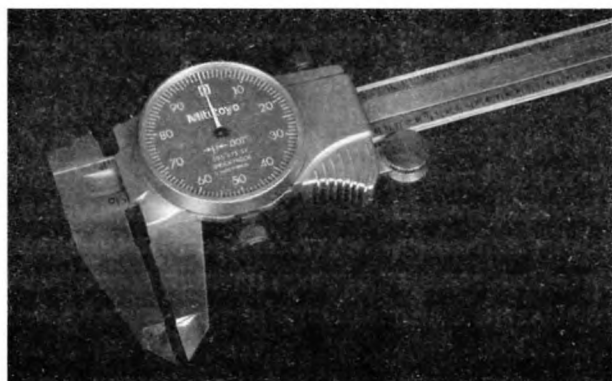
Штангенциркуль может измерять внутренний и наружный диаметры
